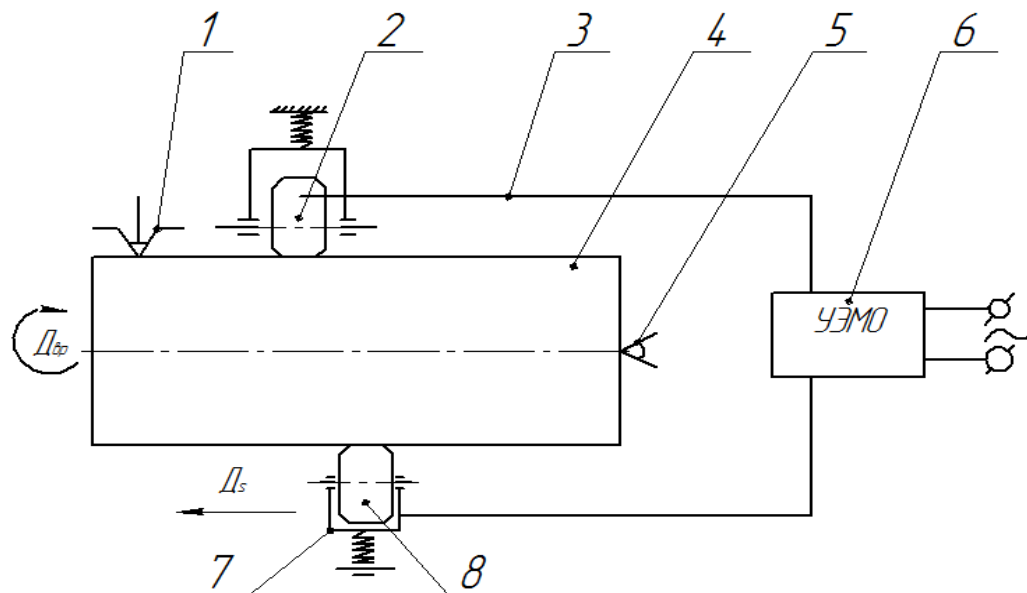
Принципиальная схема электромеханической обработки цилиндрической заготовки на токарно-винторезном станке: 1 – патрон токарно-винторезного станка; 2 – токоподводящий ролик; 3 – токопроводящая шина; 4 – заготовка; 5 – вращающийся центр; 6 – установка ЭМО; 7 – державка; 8 – инструментальный ролик
